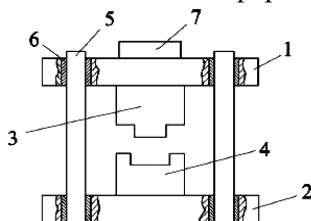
Типовая конструкция штампа для объемной штамповки:
